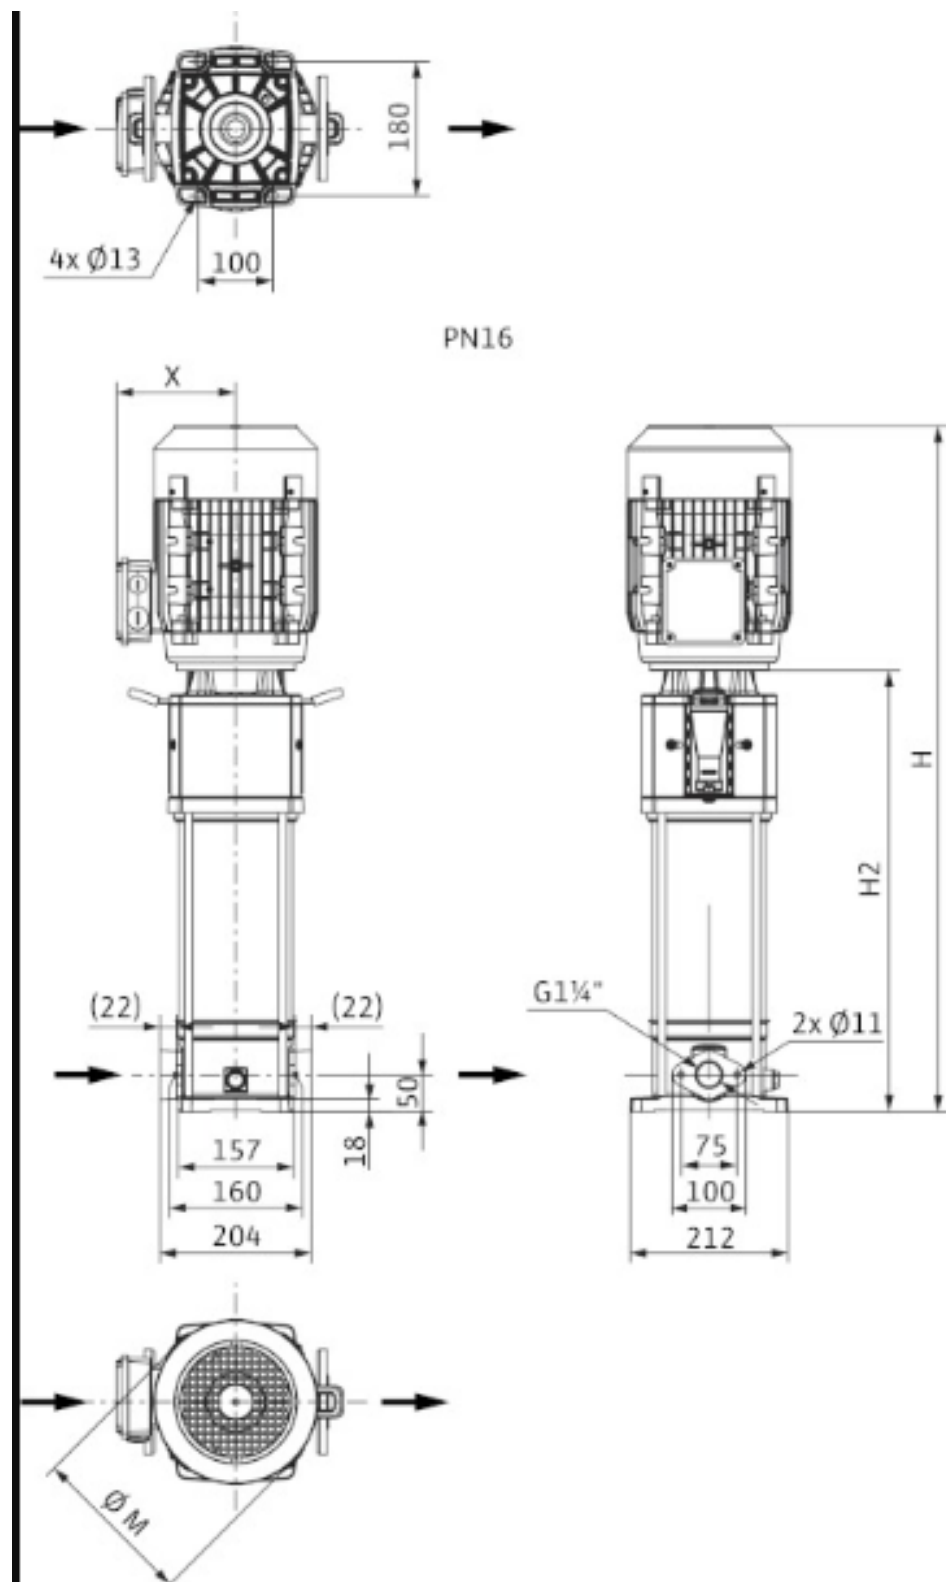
Габаритный чертеж WILO HELIX V 603-1/16/E/S/400-50
